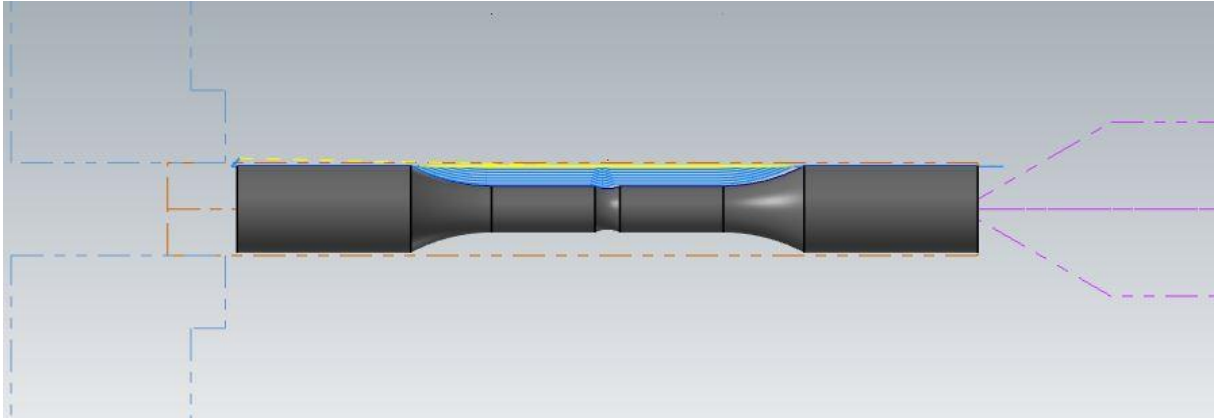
Caminhos de usinagem do CP cilíndrico entalhado
